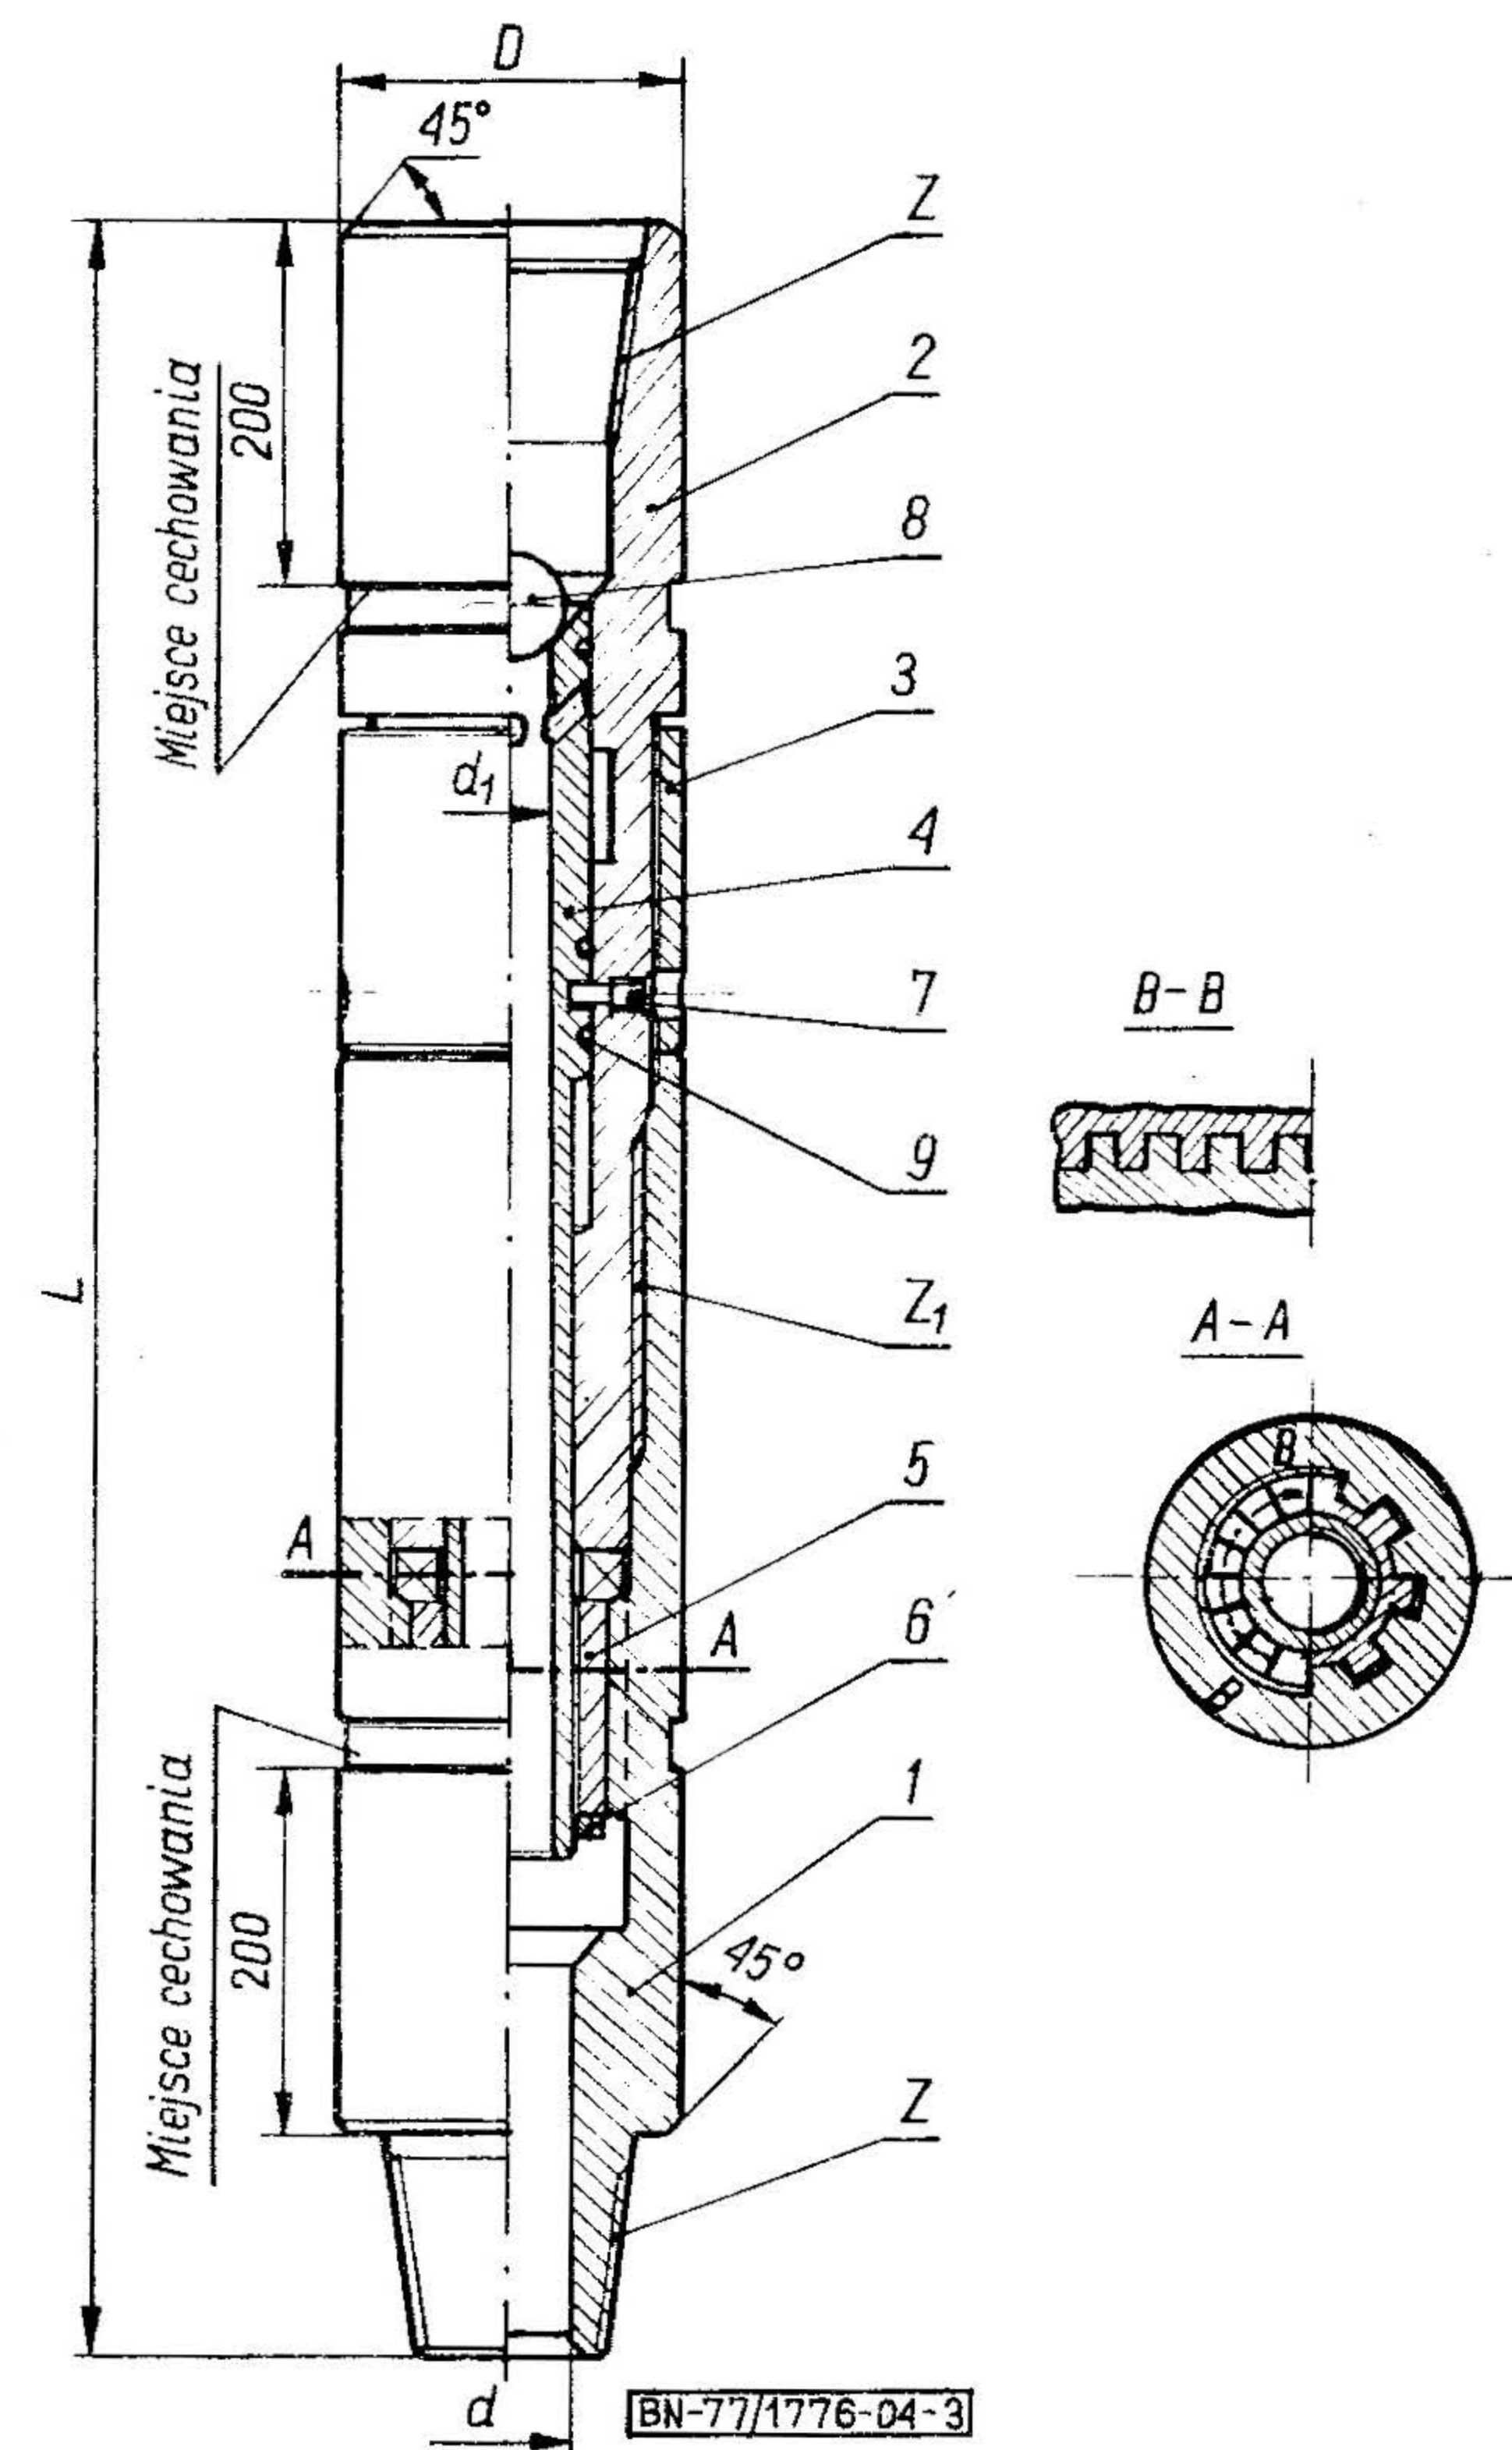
Przykładowa konstrukcja łącznika bezpieczeństwa M
